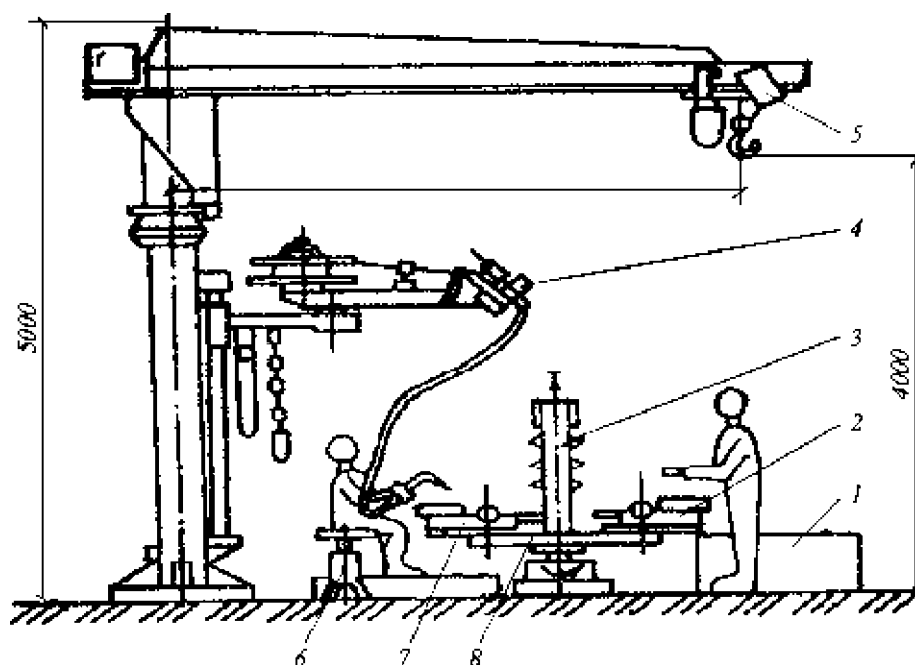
Сварочный пост для оборонно-сварочных работ (сварщик, слесарь-сборщик): 1 - складочное место для заготовок; 2, 7 - сборочно-сварочные приспособления; 3 - ширма с встроенной вентиляцией; 4 - полуавтомат с консолью; 5 - кран консольно-поворотный; 6 - стул поворотный; 8 - стол двухпозиционный поворотный
